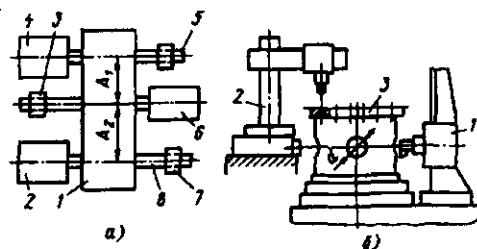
Установки для параллельной обработки поверхностей крупногабаритных деталей
